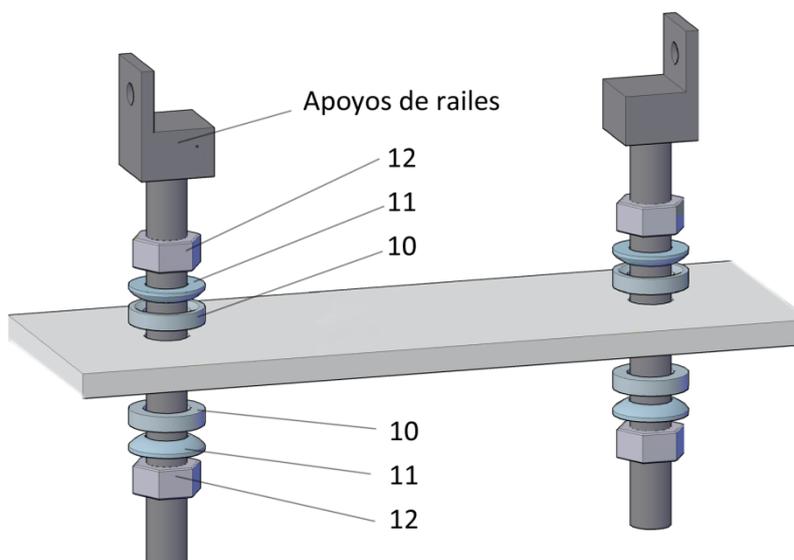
Instalación de las piezas de apoyo de la extensión de raíles.
